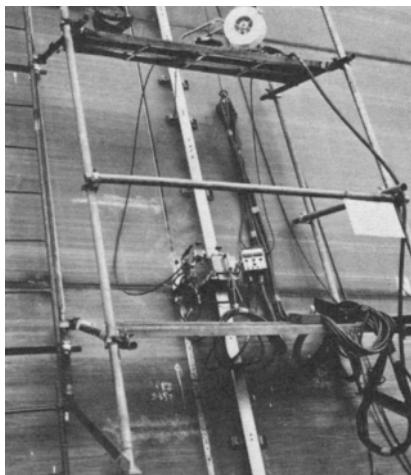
エレクトロガス溶接（造船の溶接—35年の歩み）
